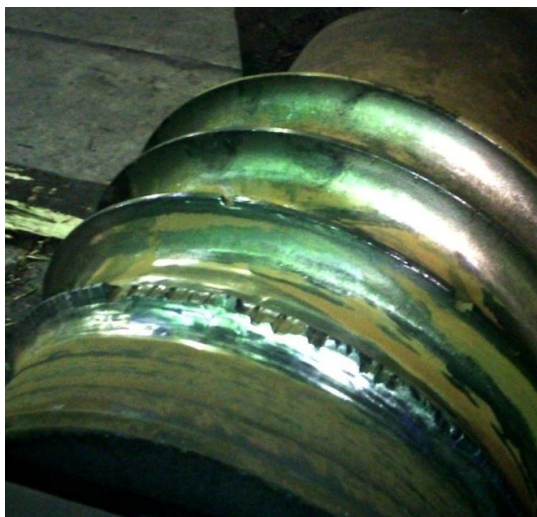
Вид изношенной поверхности и разрушения реборд валков в зоне захвата
